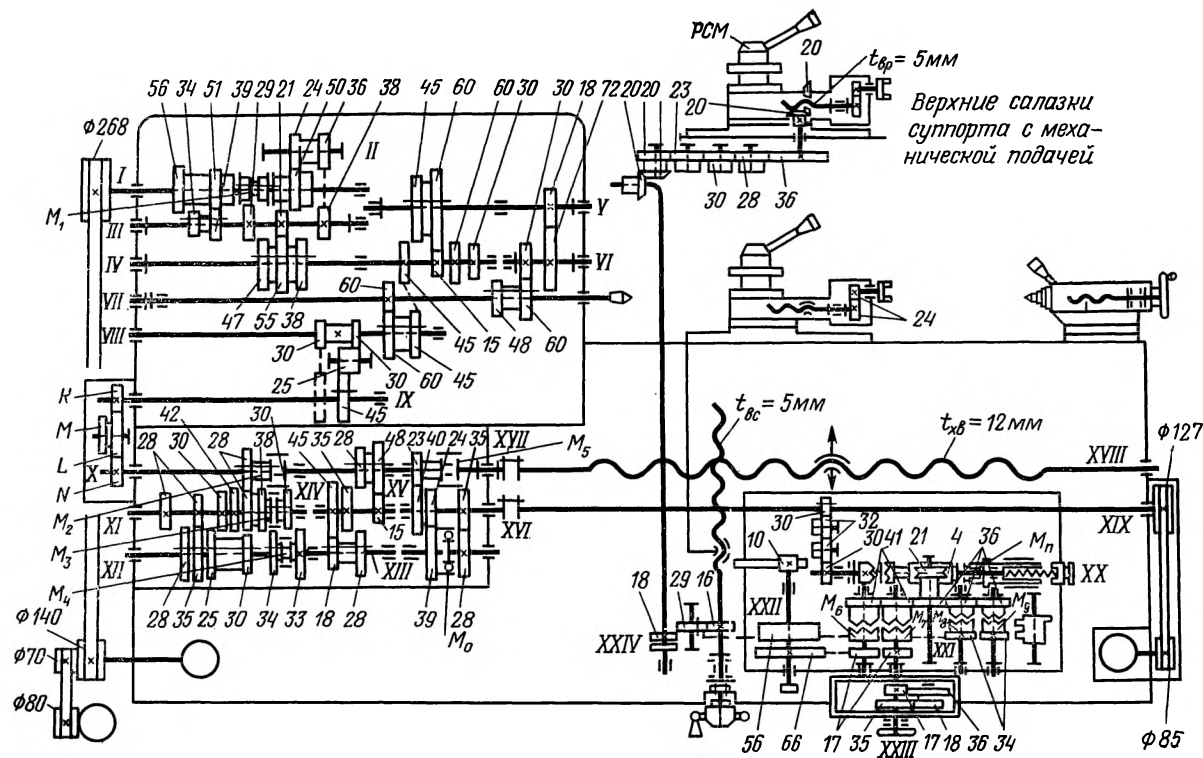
Кинематическая схема токарно-винторезного станка модели 16К20 (цифры у зубчатых колес обозначают число зубьев)
